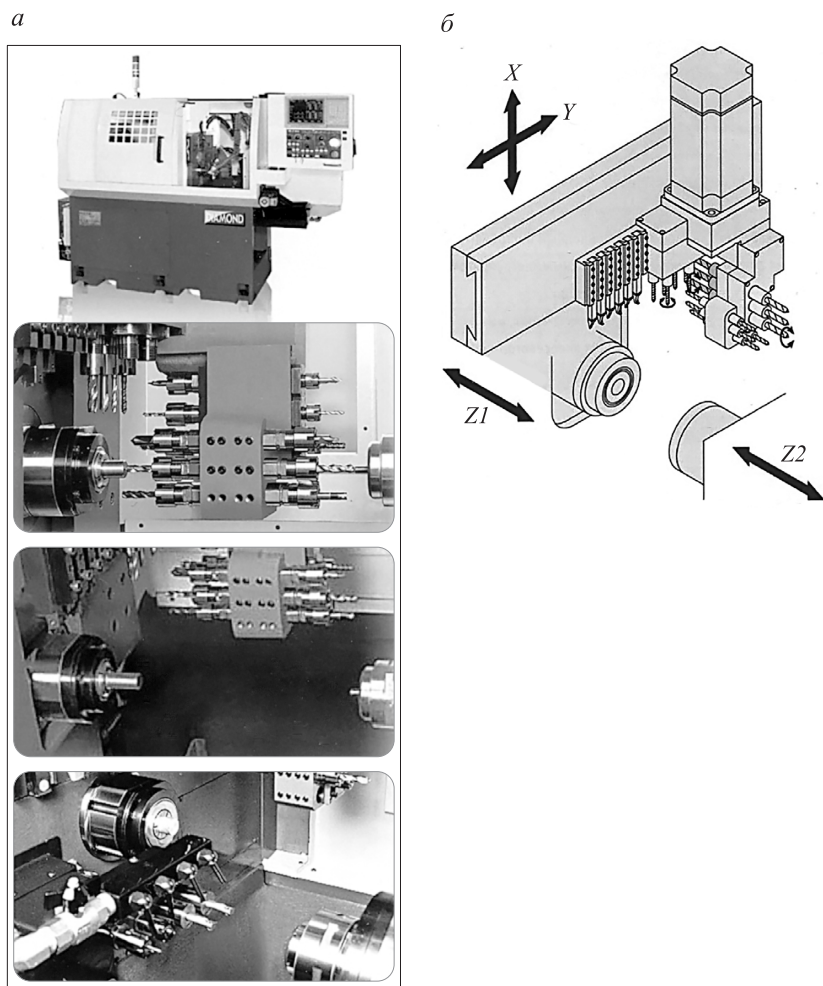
Токарный обрабатывающий центр с ЧПУ 20/32
